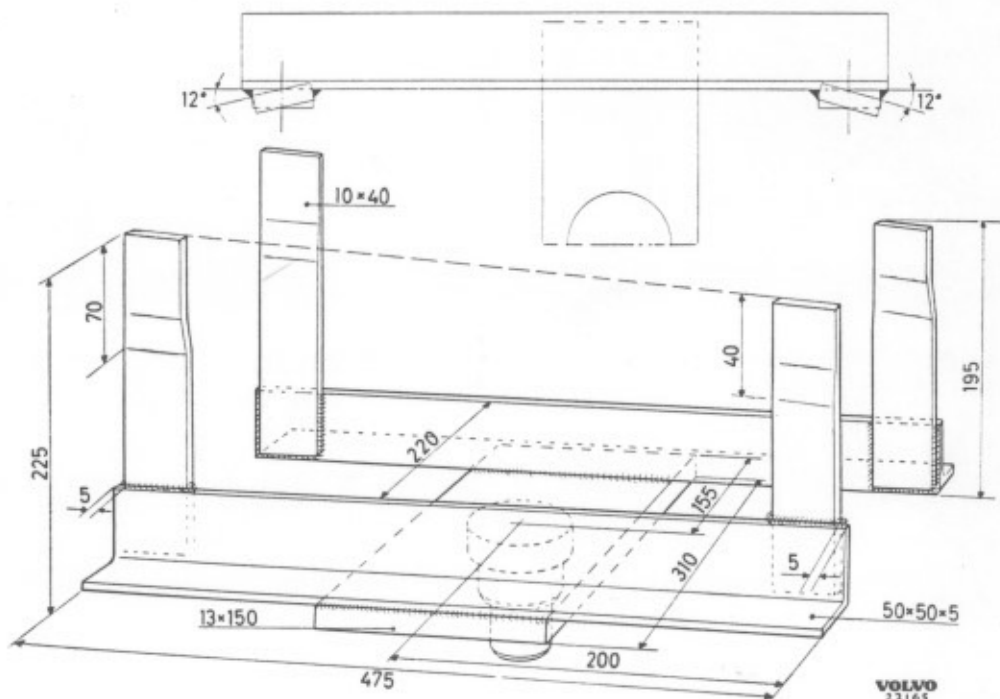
Skiss för tillverkning av demonteringsverktyg för motorn
